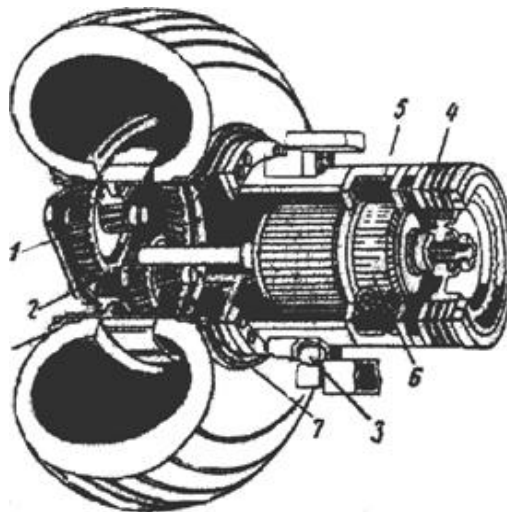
Мотор-колесо: 1 – планетарний редуктор; 2 – провідна шестірня; 3 – підшипник; 4 – система охолодження; 5 – статор; 6 – ротор; 7 – відомий зубчастий вінець; 8 – пневмошина
